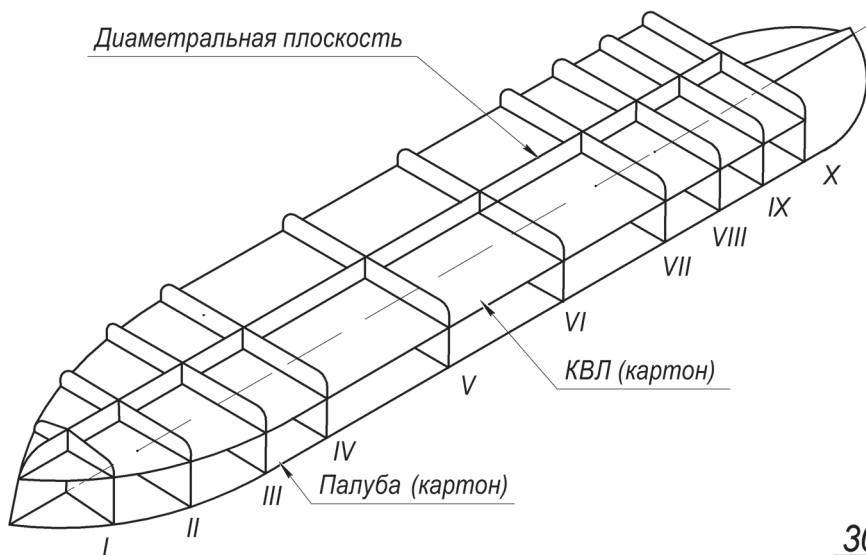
Схема сборки остова корпуса парохода «Ваня».
